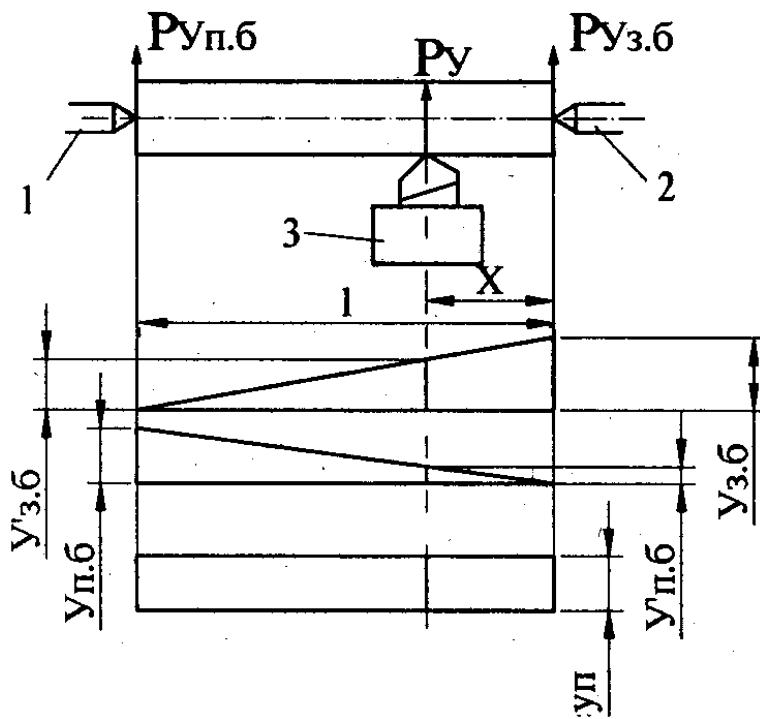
Схема нагрузки и упругих перемещений узлов станка при обработке вала в центрах: 1 – передняя бабка; 2 – задняя бабка; 3 - суппорт
